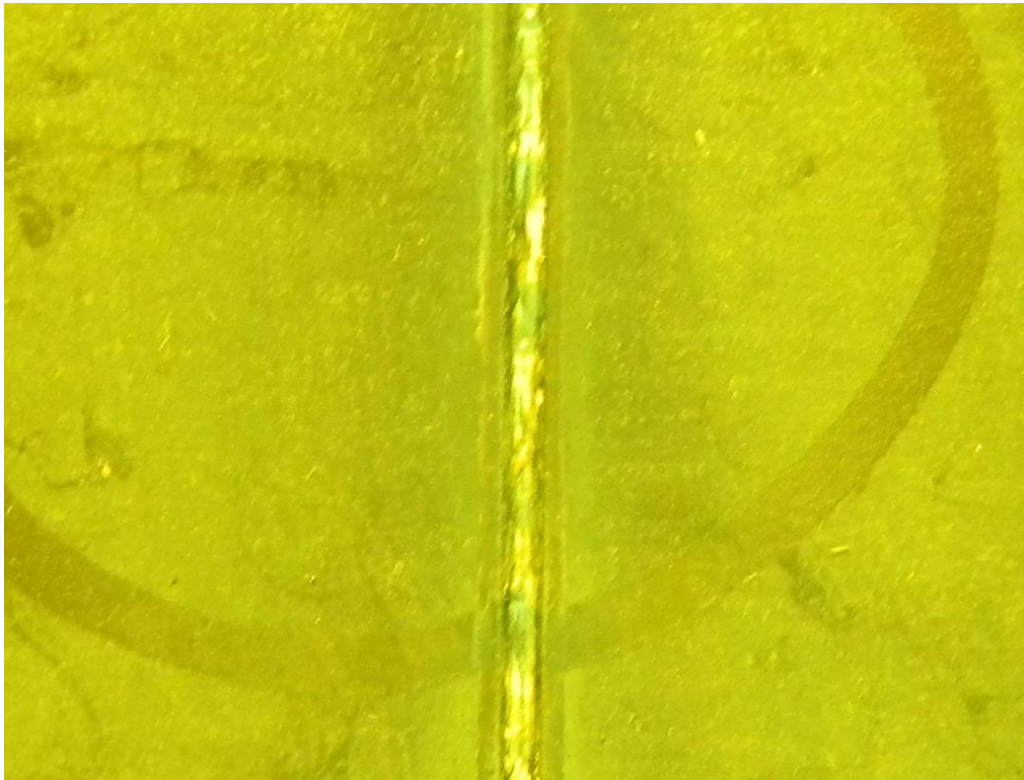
Образец после сварки подготовленный лазерной резкой
